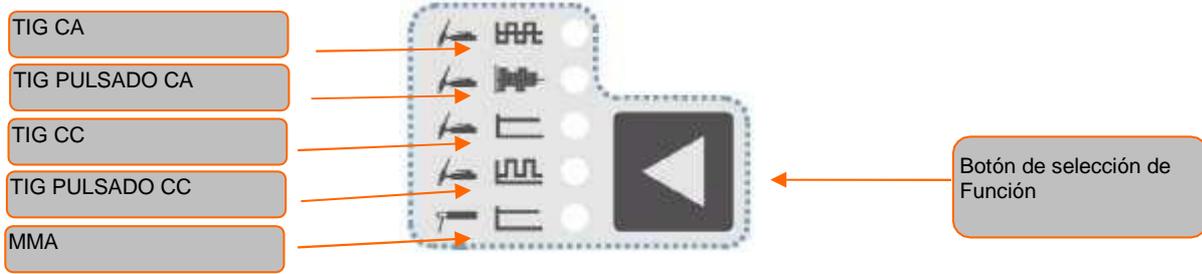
Descripción panel de selección modo de soldadura
